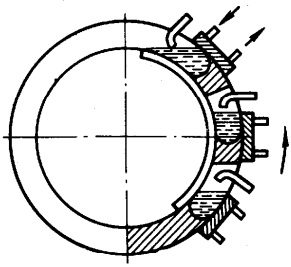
Схема автоматической сварки шва резервуара с принудительным формованием (без вращения)
